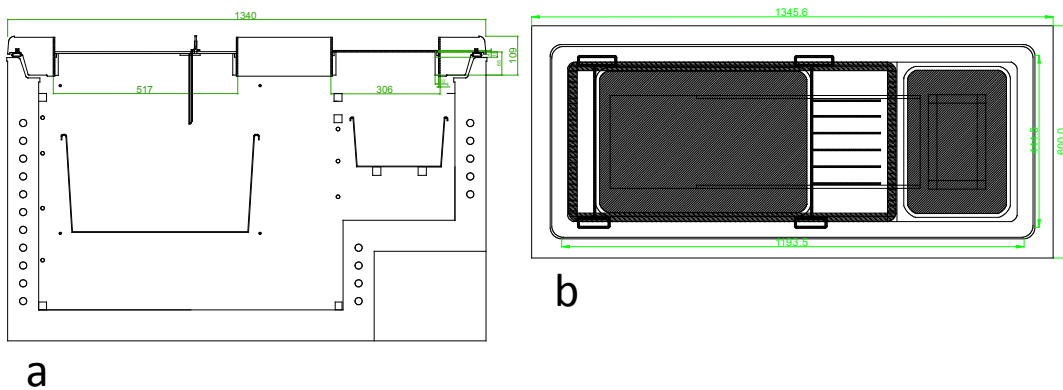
Camera climatica a: sezione trasversale con predisposizione per un singolo test; b: planimetria con vista del lume interno.
